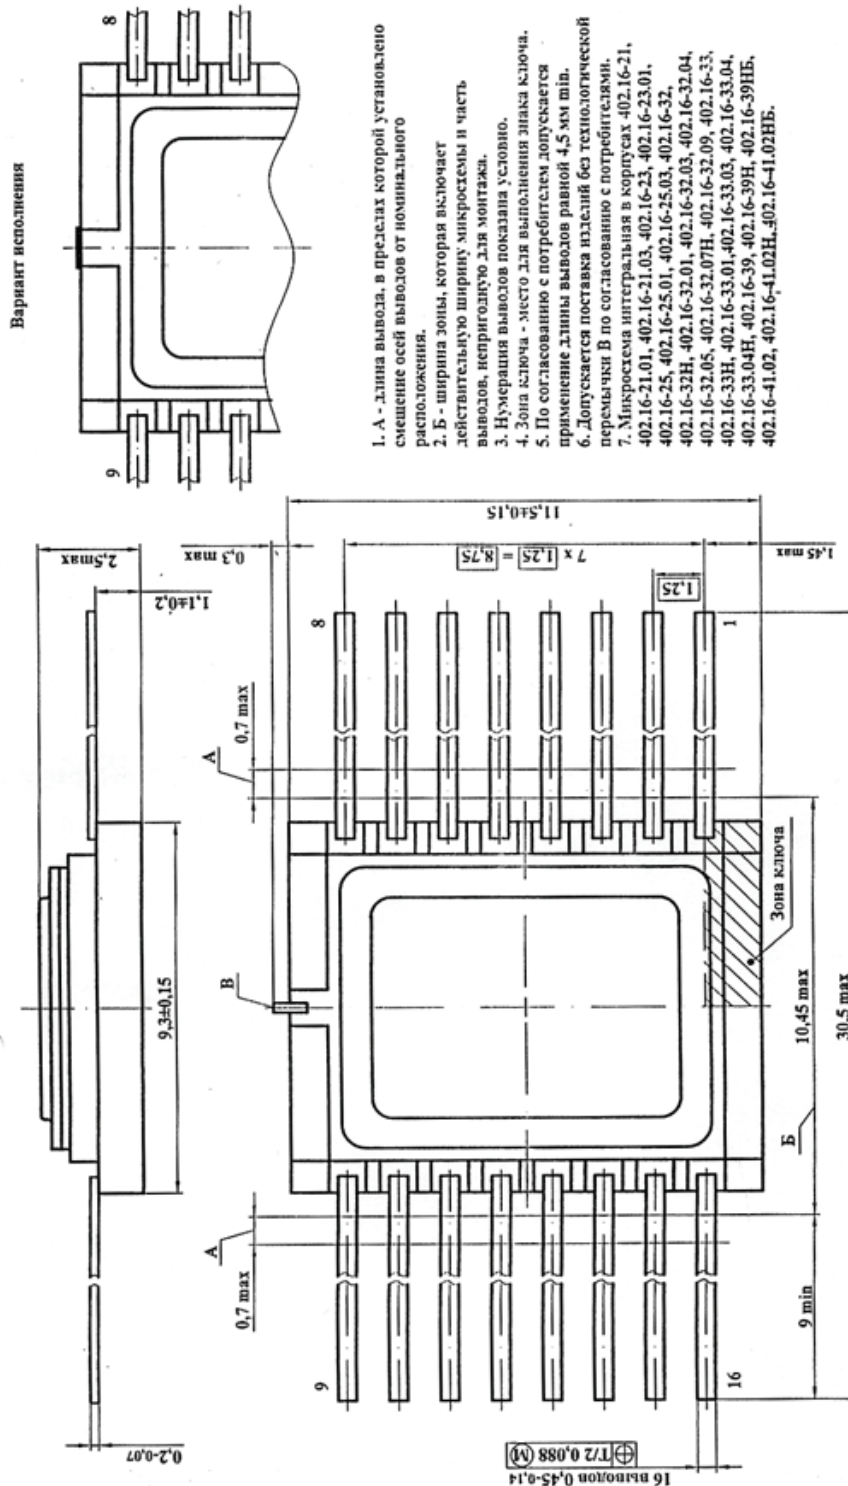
Габаритный чертеж корпуса 402.16-21
